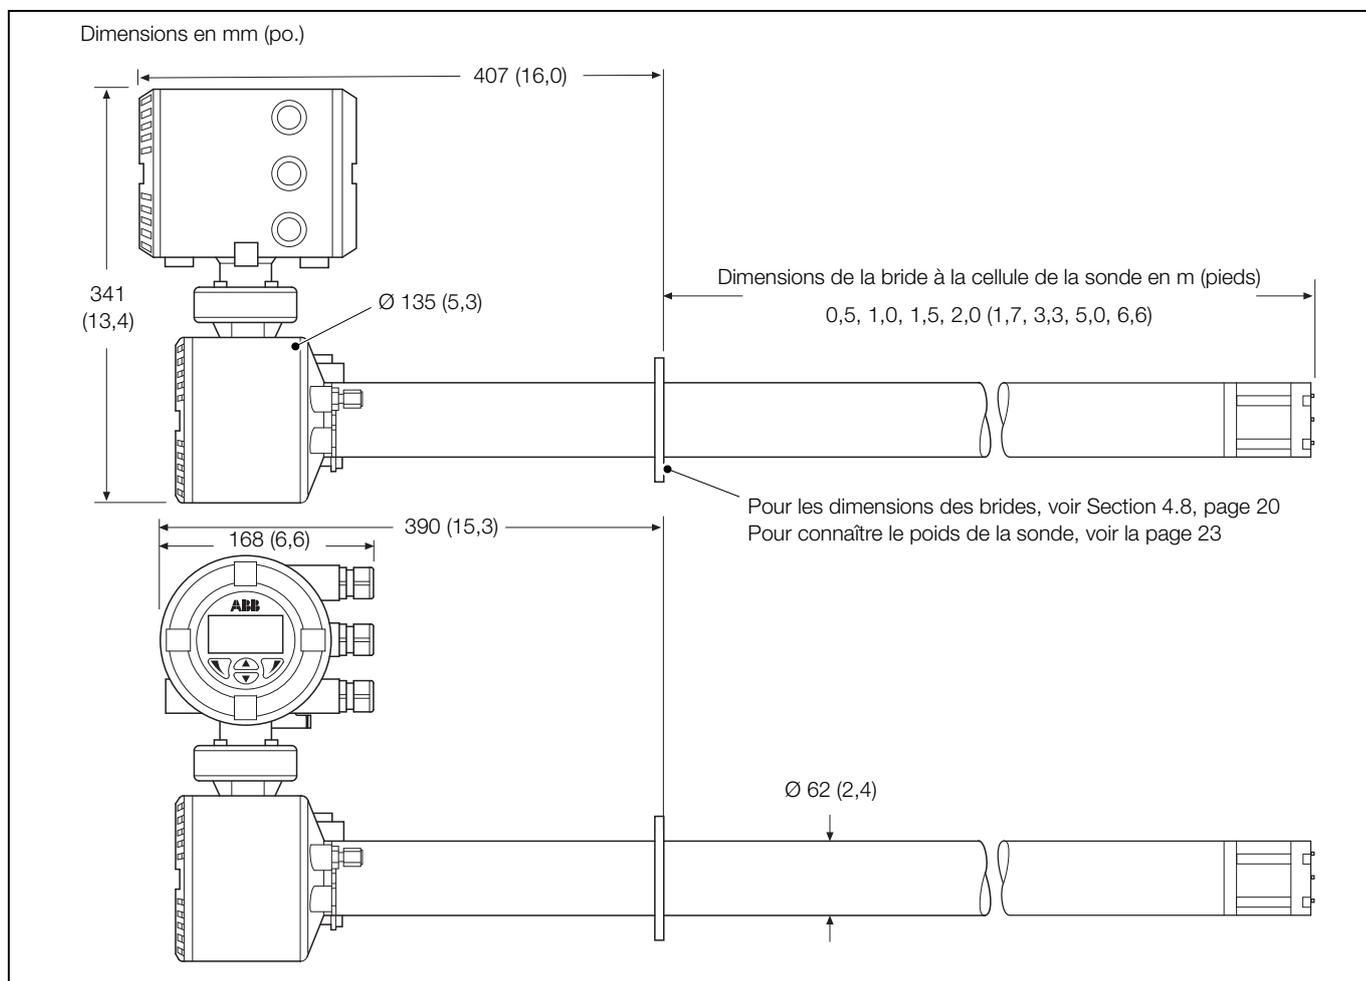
Dimensions générales – Sonde Endura AZ30 intégrée
